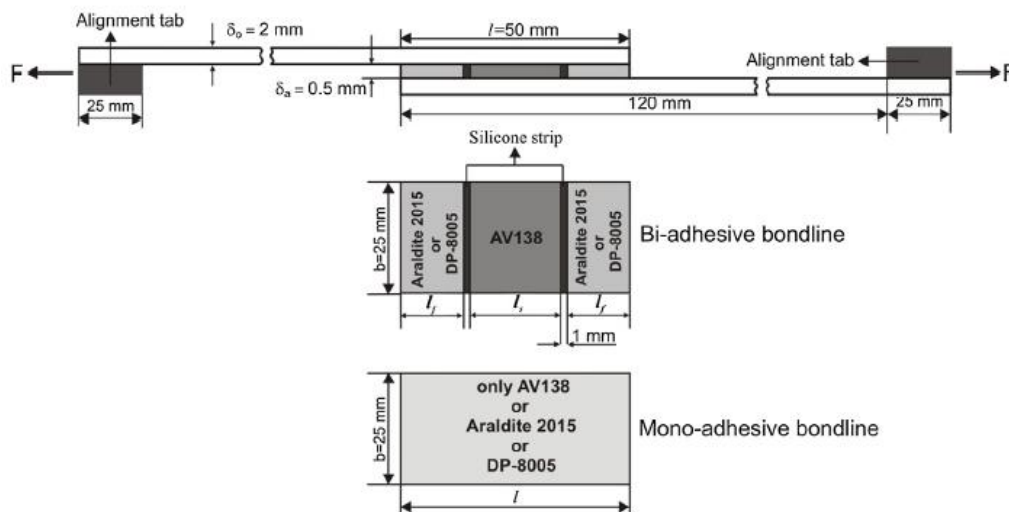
Geometria e dimensões das juntas com um e dois adesivos [56].
